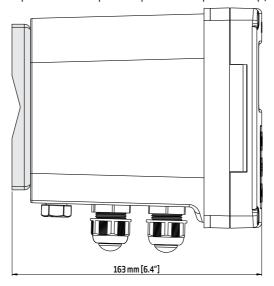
Controlador HI510 acoplado al panel para montaje en la pared
